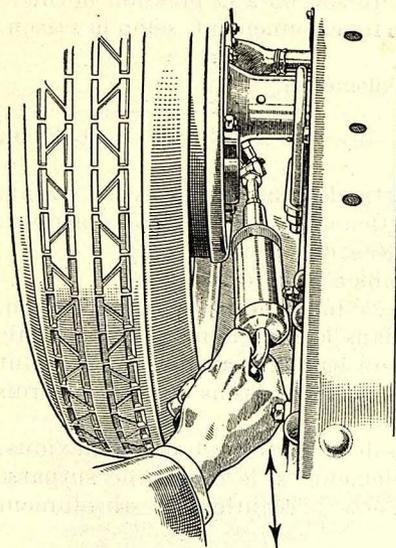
Graissage des roulements extrêmes du pont arrière.
